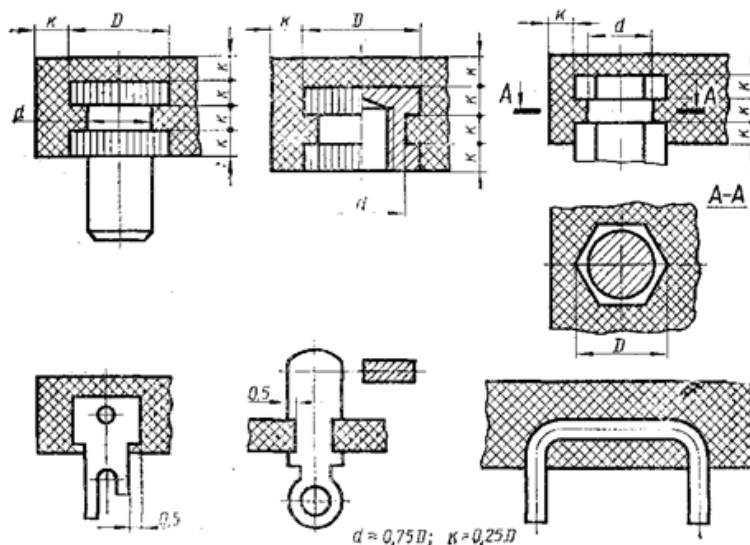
Обозначение материалов на сборочном чертеже
